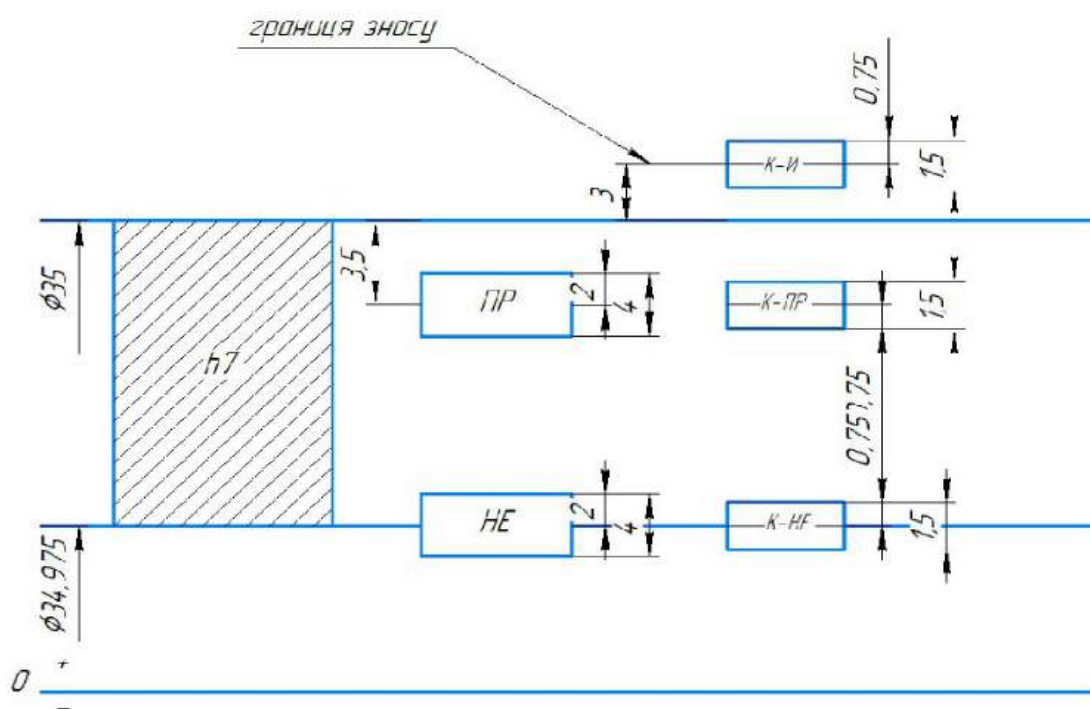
Схема розташування полів допусків вала, калібру-скоби й контркалибрів
